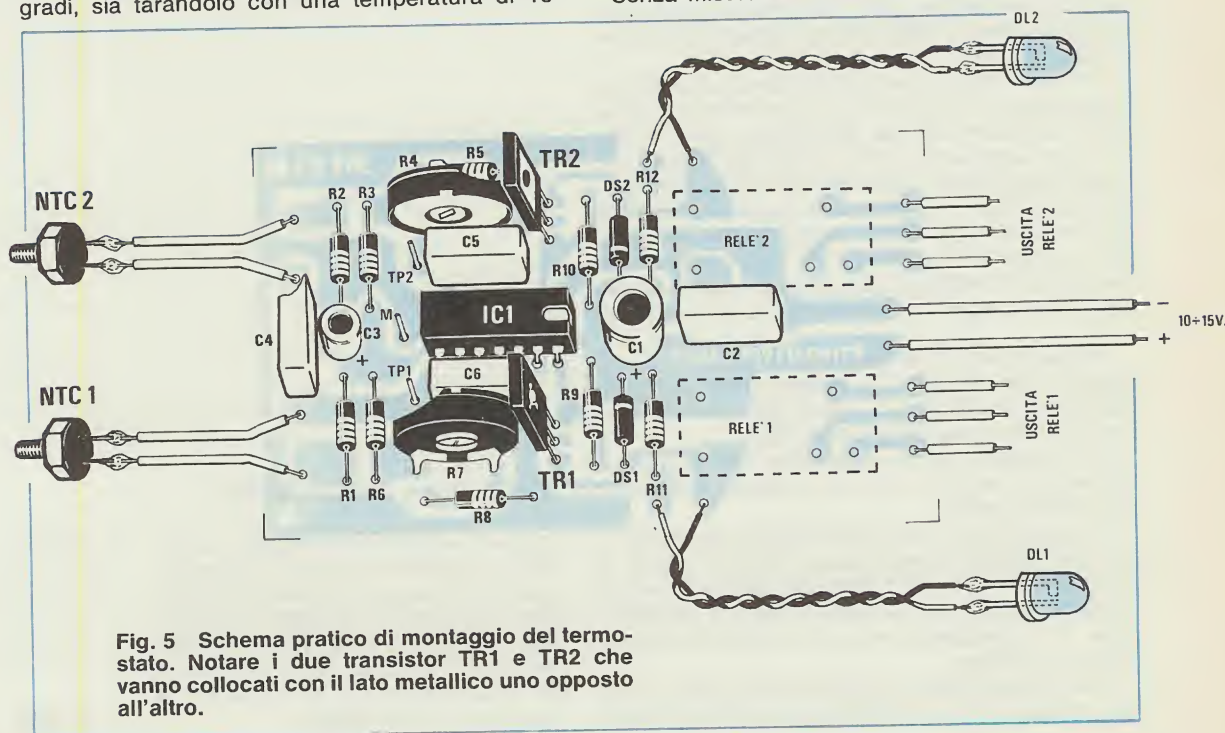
Schema pratico di montaggio del termostato. Notare i due transistor TR1 e TR2 che vanno collocati con il lato metallico uno opposto all'altro.
